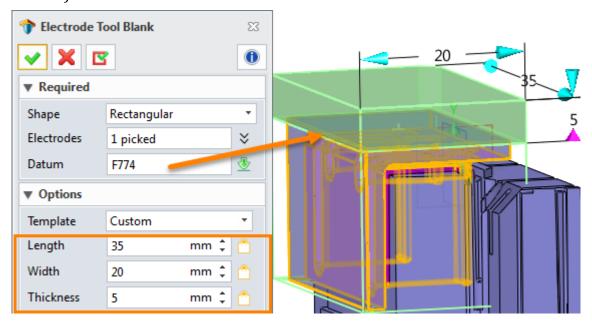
dimensión básica para el blank de grupo de electrodos 3
